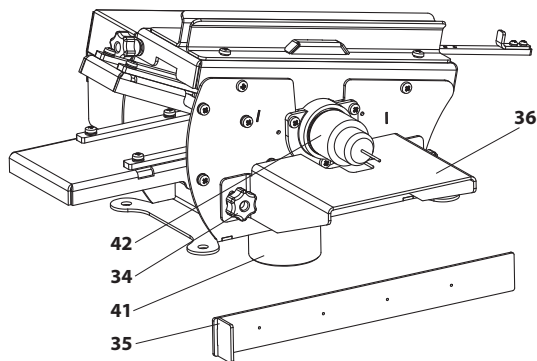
Общий вид приставки с установленным сверильным патроном
